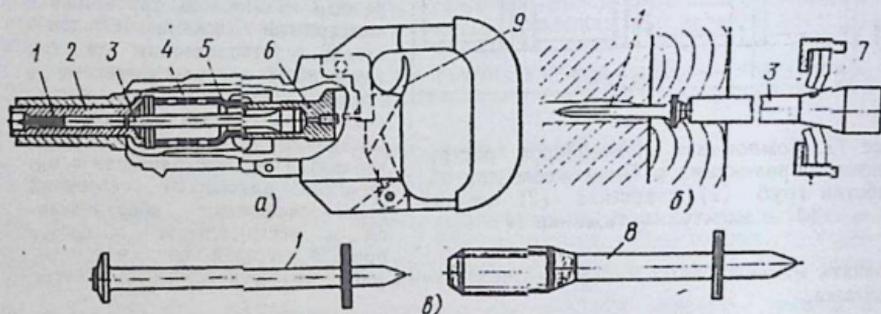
Поршневой монтажный пистолет ПЦ52-1:
